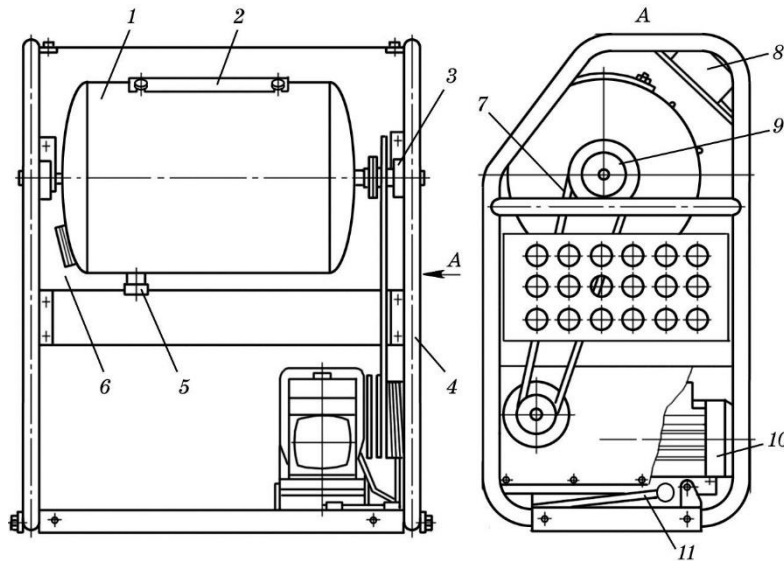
Схема масловиготовлювача МИП-1500:
